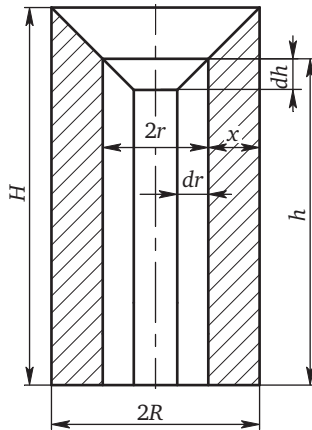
Схема к расчету усадочной раковины в цилиндрической отливке
